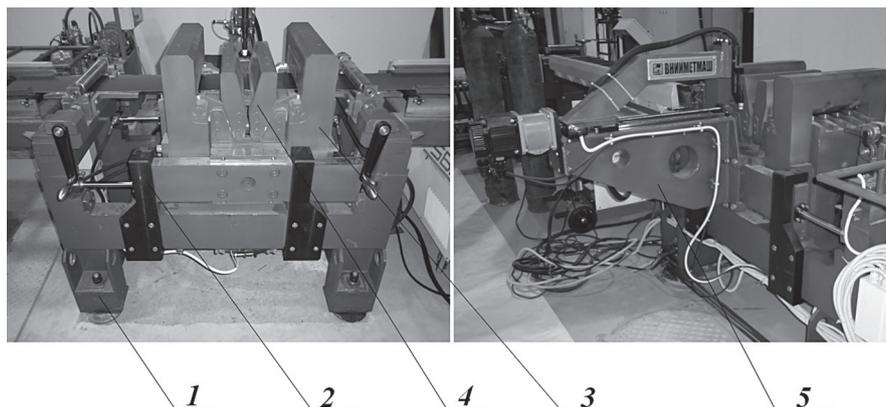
Установка стыкосварочная: 1 – рама; 2 – направляющая; 3 – ножницы; 4 – прижим полосы; 5 – сварочная консоль
